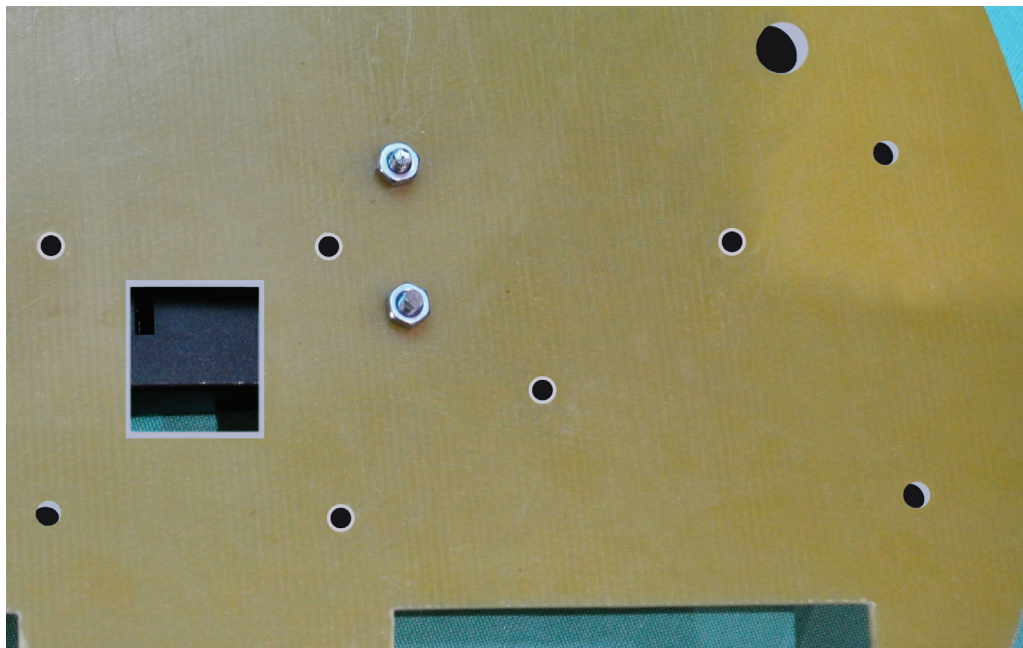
Аккумуляторный бокс прикреплен винтами к корпусу (верх корпуса)
